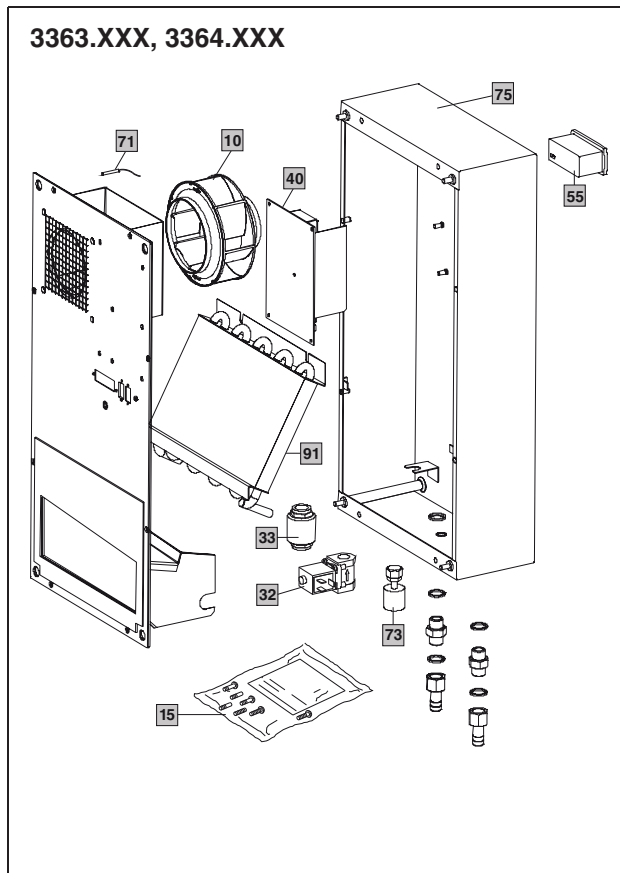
Ersatzteile 3363.XXX, 3364.XXX
